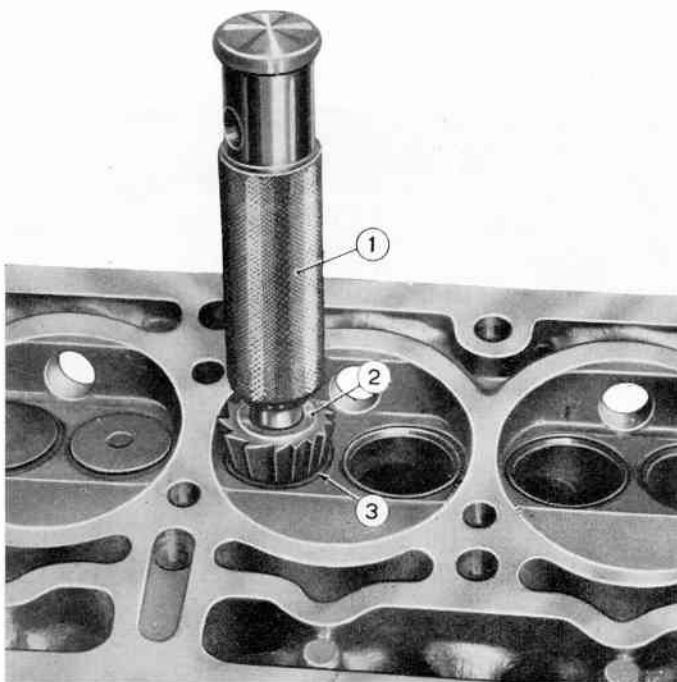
Verminderung der Ventil Sitzbreite mit dem 75°-Fräser A. 94030 mit Spindel A. 94058.
